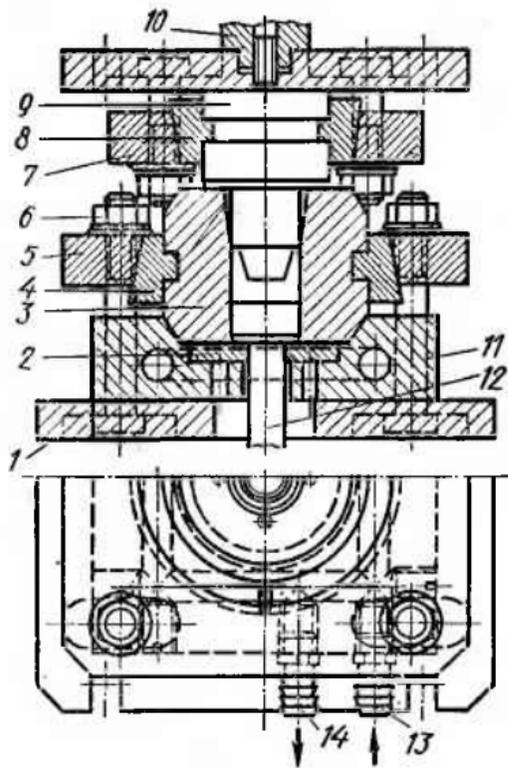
Штмп фрикционного пресса для изготовления поковки колпачка
